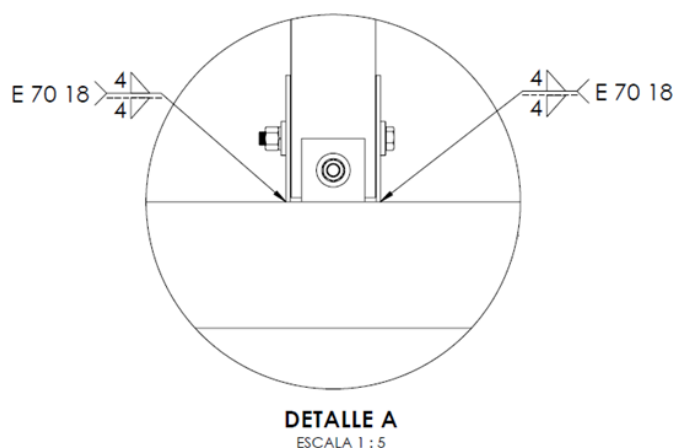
Soldadura a filete a doble lado con un lado efectivo de 4 mm
